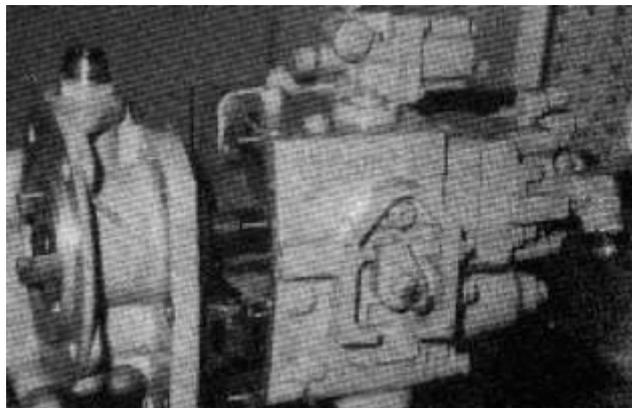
DESMONTAJE DE LA CUBIERTA DEL IMPULSOR DELANTERO
